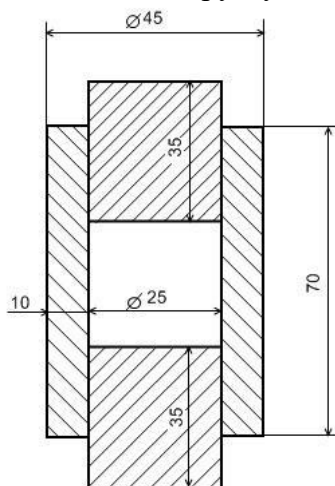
Форма для приготовления образцов из смеси битума и минерального порошка
